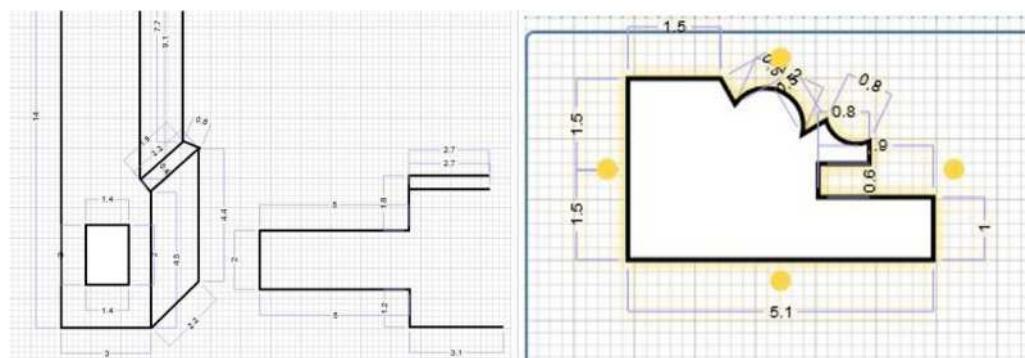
Planimetría de estructura del marco. Aut.: Alejandra del Barrio Luna.
